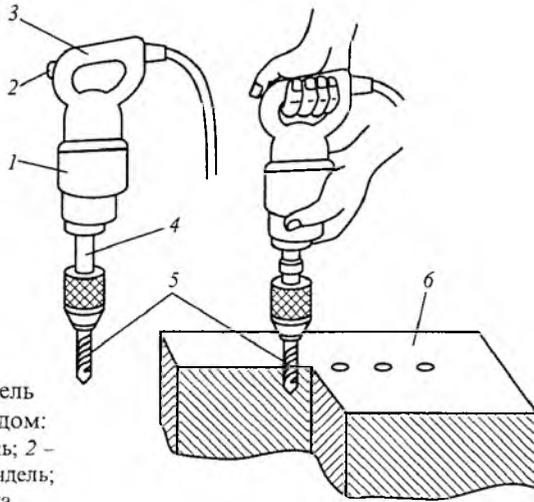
Резьбонарезатель с пневматическим приводом:
